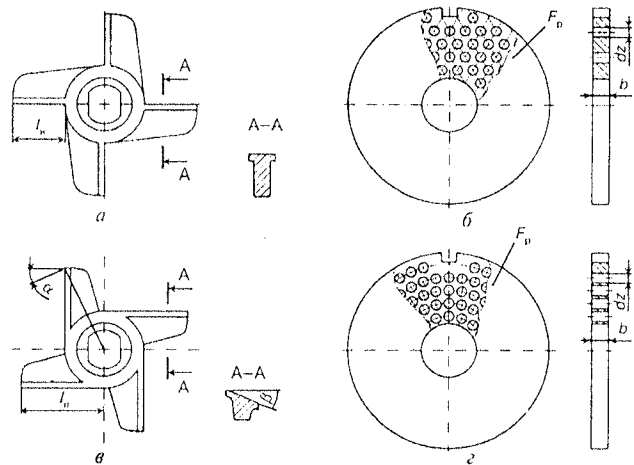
Схемы режущих инструментов: а — серийный нож; б — серийная решетка; в — новый нож; г — новая решетка
